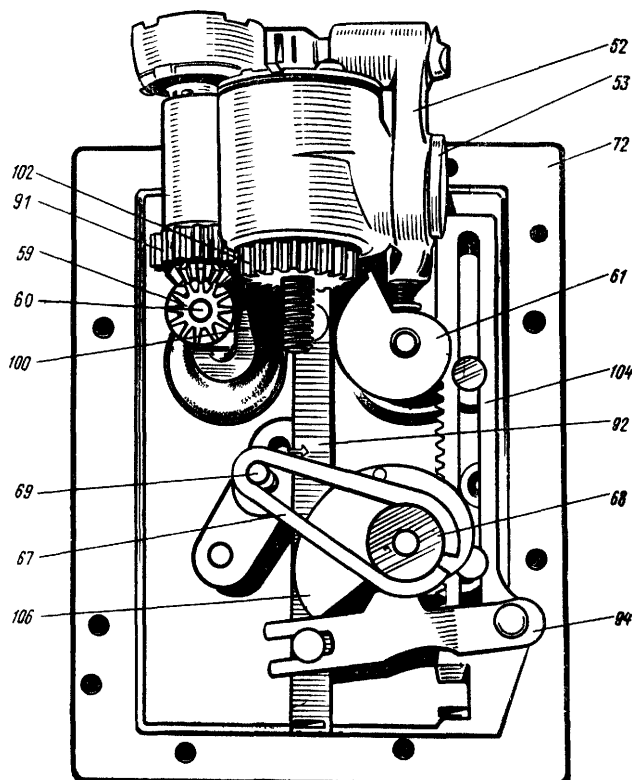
53—ось рычага а регулировки степени неравномерности; 54 — рычаг регулировки степени неравномерности; 59—шестерня механизма настройки частоты вращения; 60—валик механизма настройки частоты вращения; 61 — кулачок регулирования степени неравномерности; 67—пружинный тормоз; 68— фрикционный диск; 69—палец пружинного тормоза; 72 — панель; 91 — вал-шестерня установки частоты вращения; 92 — планка ограничителя нагрузки; 94 — профильный рычаг ограничителя нагрузки; 100 — винтовой шток; 102 — скользящая шестерня-гайка; 104 — зубчатая рейка; 106 — кулачок ограничения нагрузки
